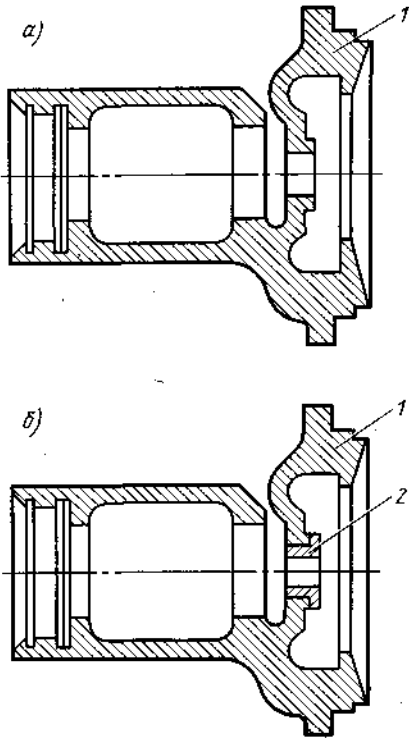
Корпус водяного насоса двигателя базовой (а) и ремонтной (б) конструкции: 1 — корпус; 2 — опорная ремонтная втулка
